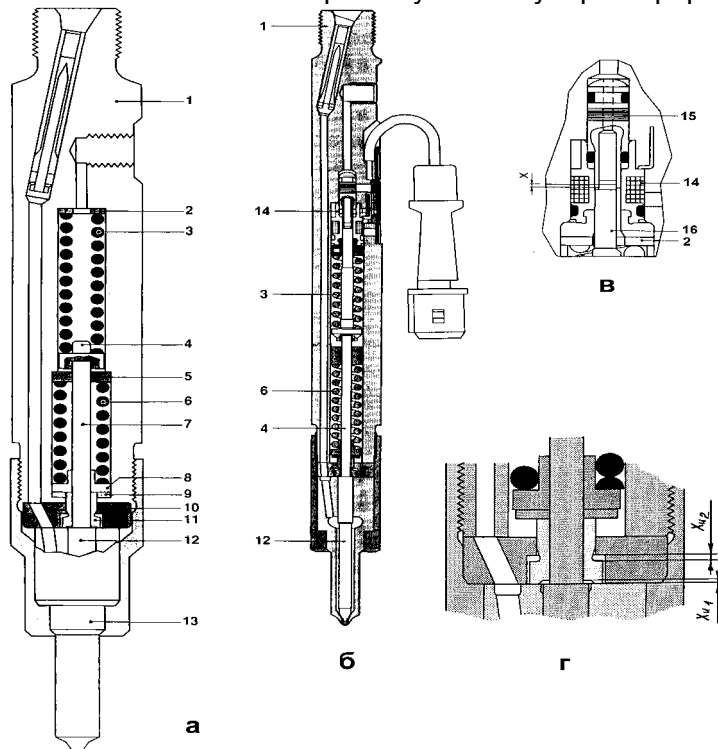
Двухпружинные форсунки R.Bosch: а - 2...4-го цилиндров; б - 1-го цилиндра; в - датчик подъема иглы; г - проставка с механизмом последовательного включения пружин.
